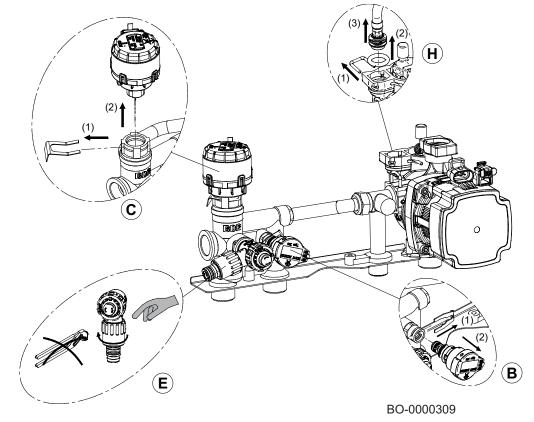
Pièces pour groupe hydraulique de la chaudière de chauffage seulement
